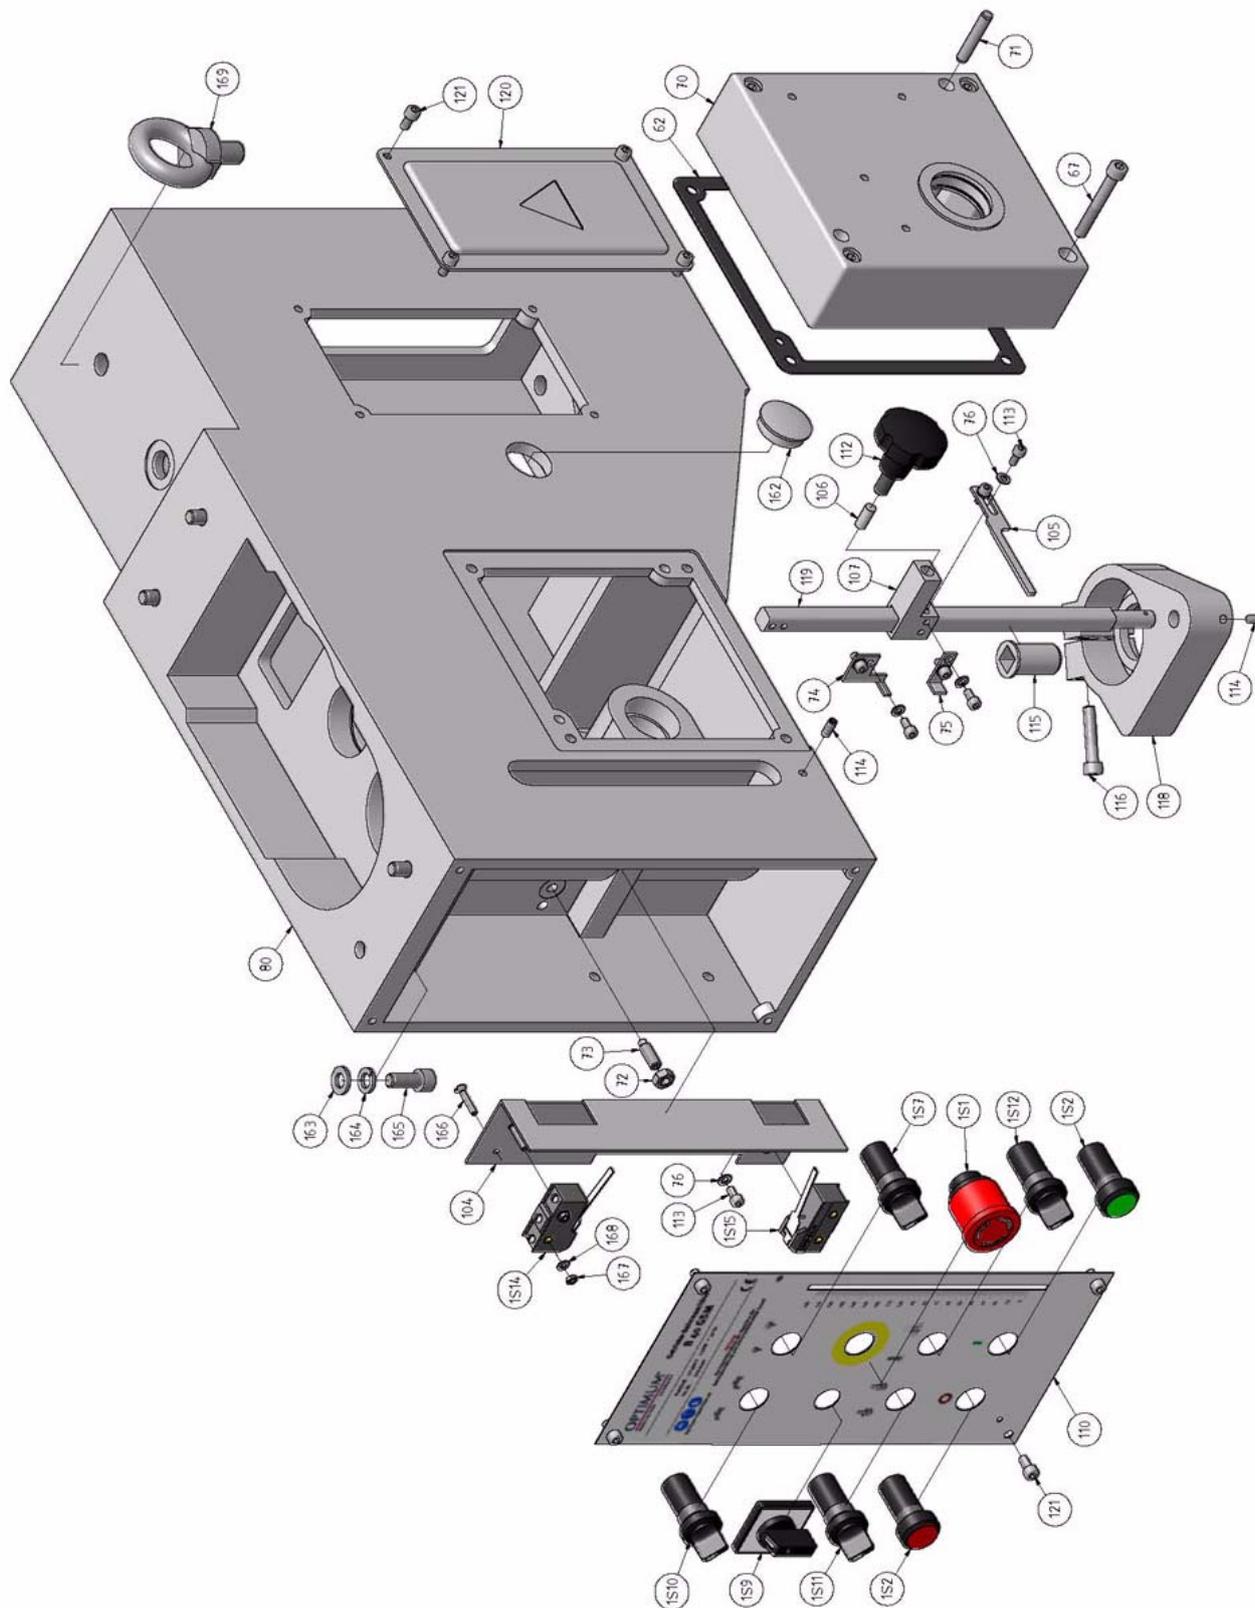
Vorschubgetriebe 3 von 4 - Feed gear box 3 of 4
